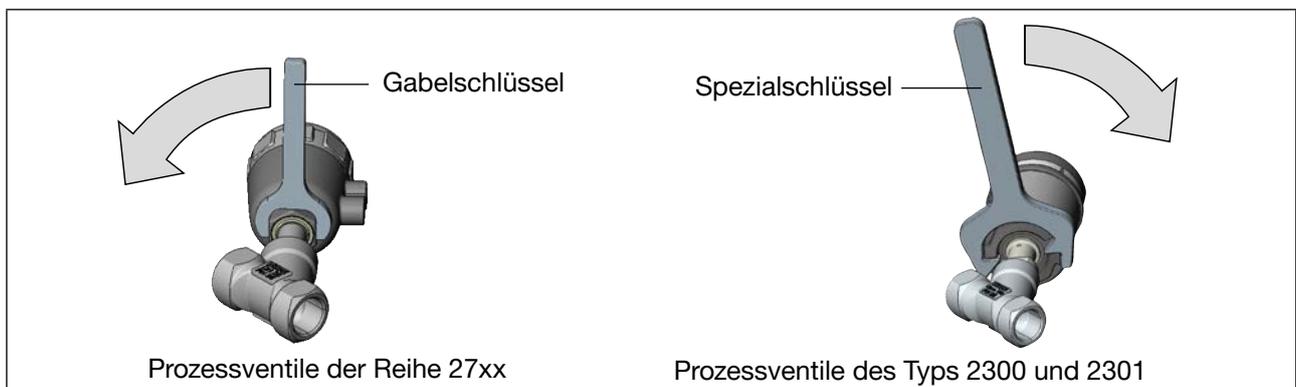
Vorgeschriebene Drehrichtung und Werkzeug für das Drehen des Antriebsmoduls
